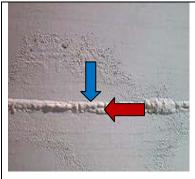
Superficie F mal soldada del tanque n
